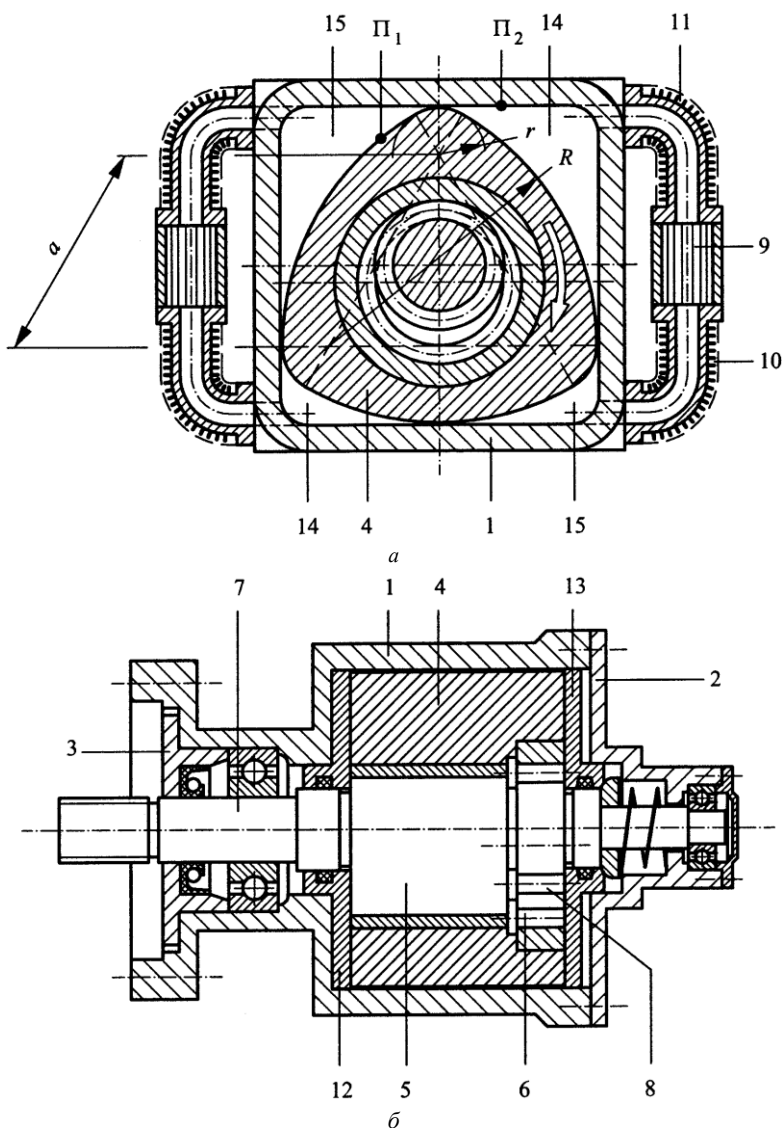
Схема роторно-поршневого двигуна з двома парами комор:
